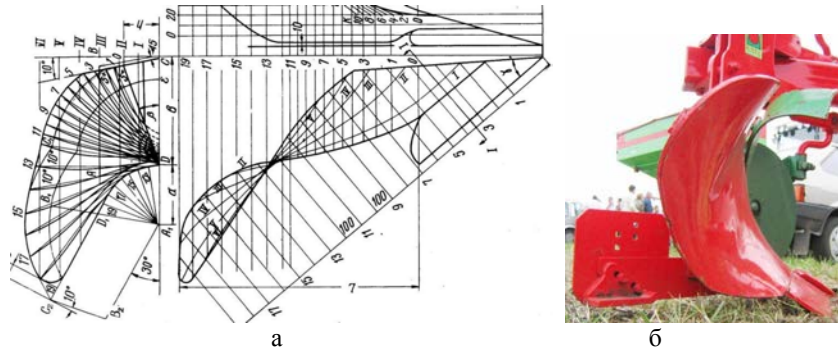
Форма робочої поверхні полицевого корпусу за Б.М. Шмельовим [3]; в – корпус плугу корпорації UNIA [«День поля» в УкрНДПВТ, 2011]
